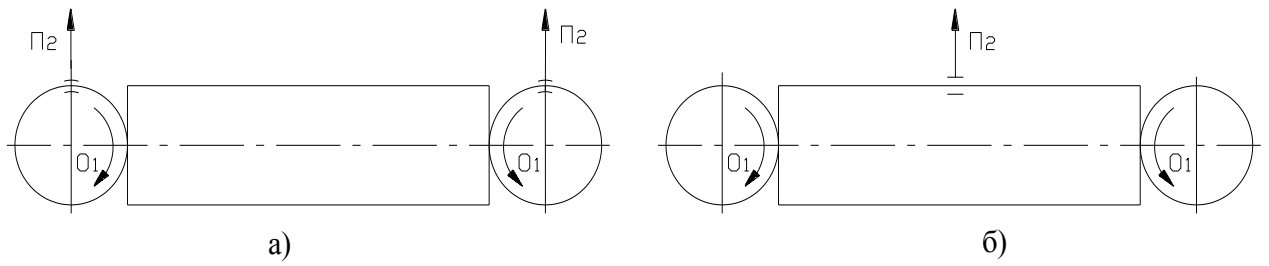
Схема обробки торців циліндричними фрезами з рухомою (б) і нерухомою (а) заготовкою
